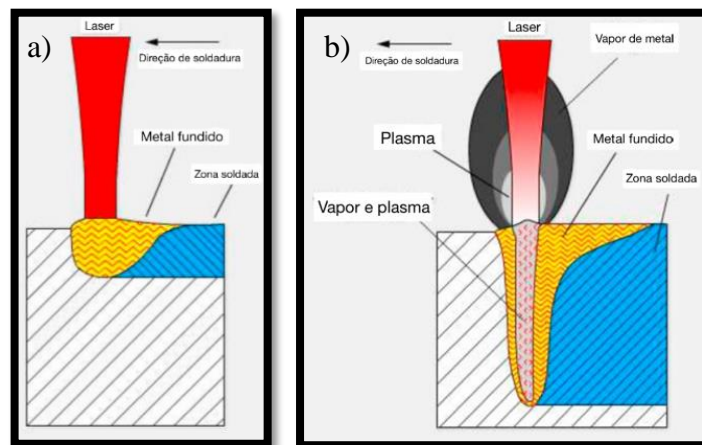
Representação dos modos de soldadura a laser a) condução b) penetração [10]
